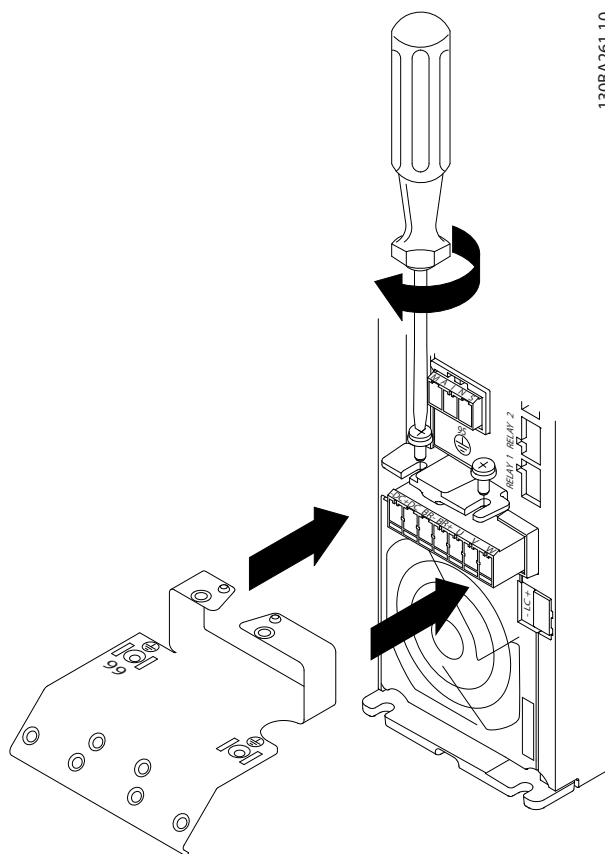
Připojení měniče k motoru, krytí H9
